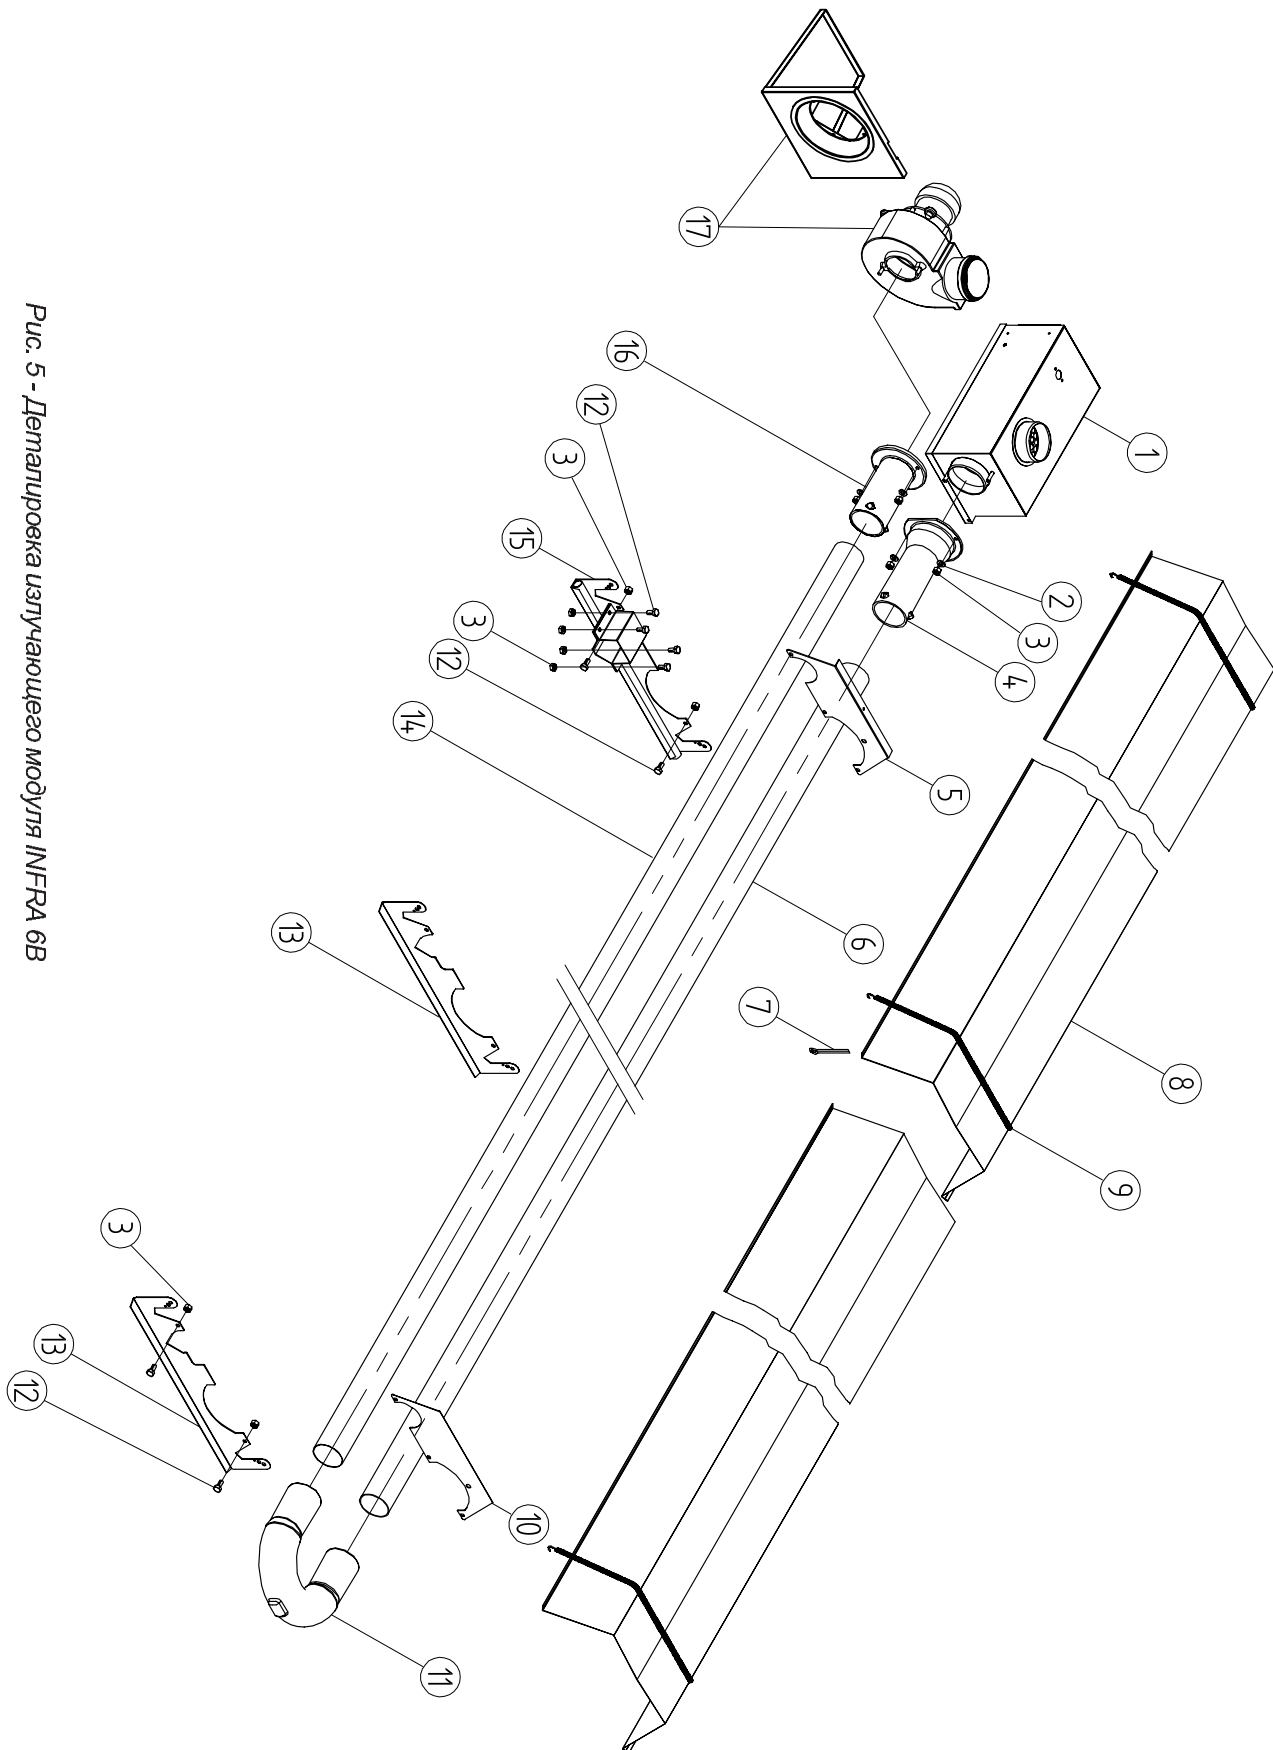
Деталировка излучающего модуля INFRA 6B
